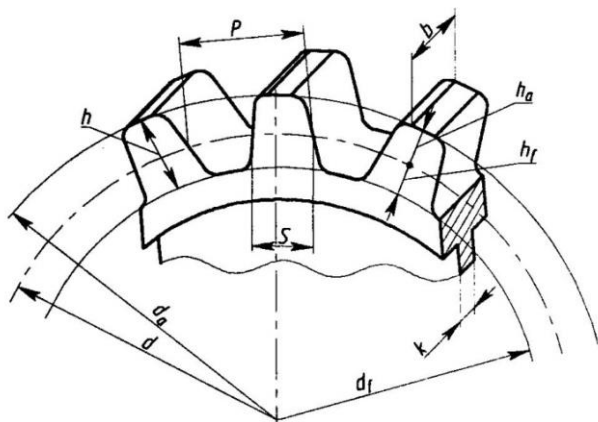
Параметры зубчатого колеса:  $P$  – шаг зубьев;
